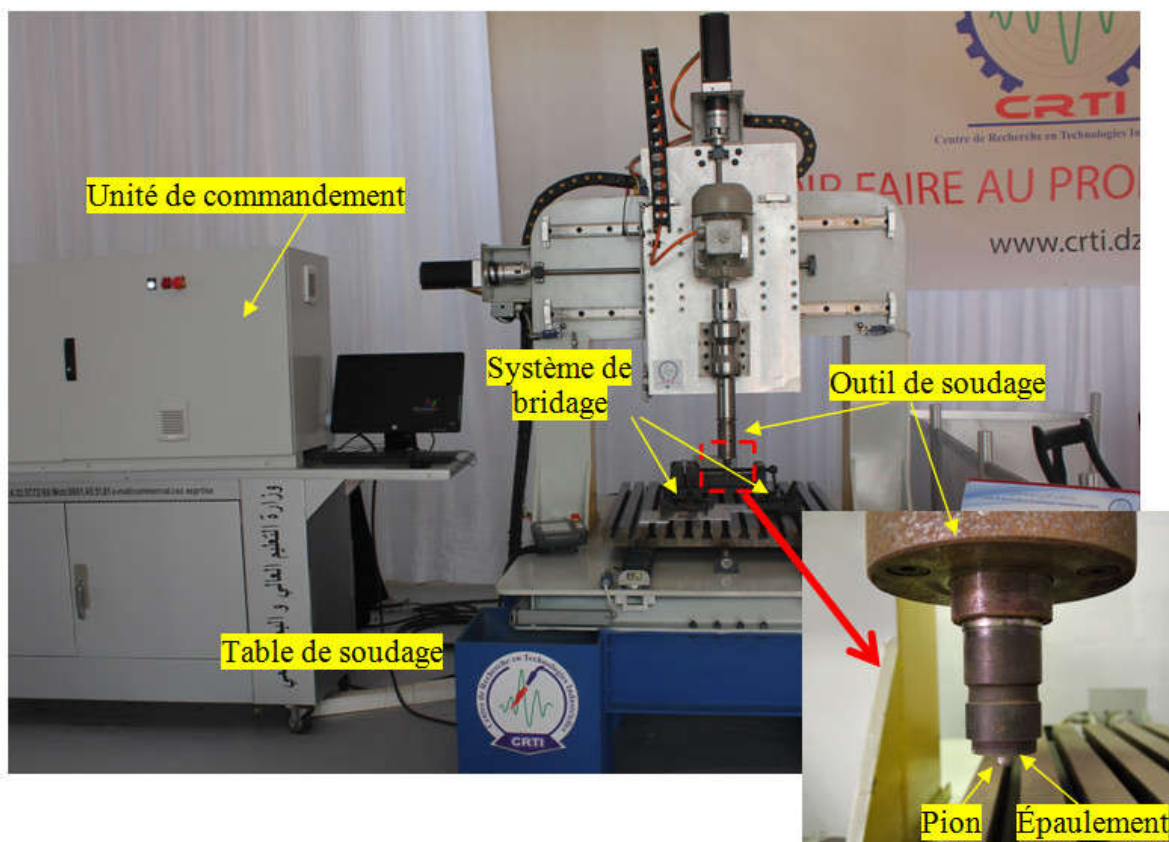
dispositif expérimentale de soudage FSW.
